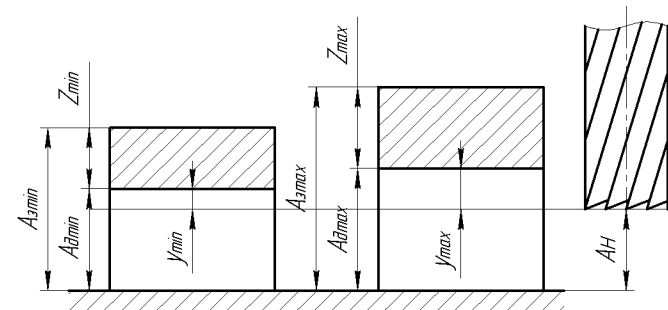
Визначення максимального і мінімального припусків при обробці на налагодженому фрезерному верстаті
